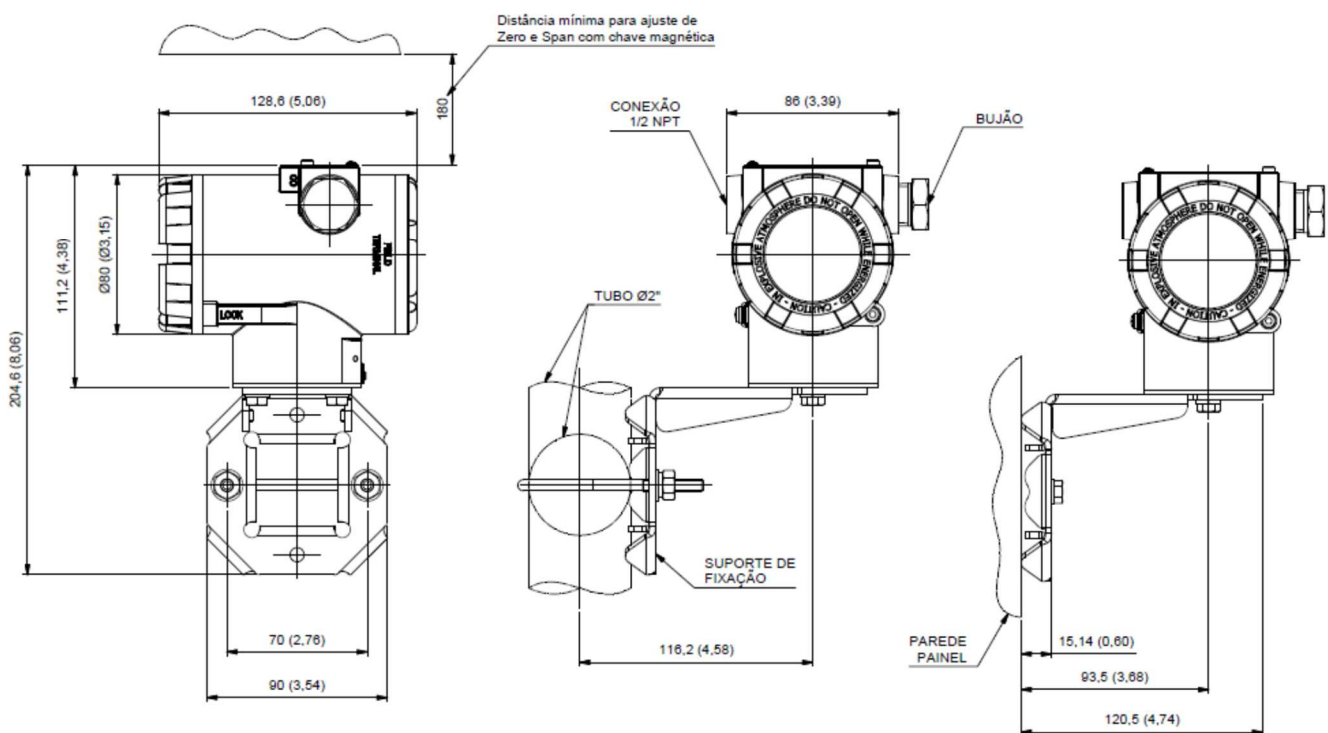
Desenho dimensional e esquema de montagem do VHC10-F.
